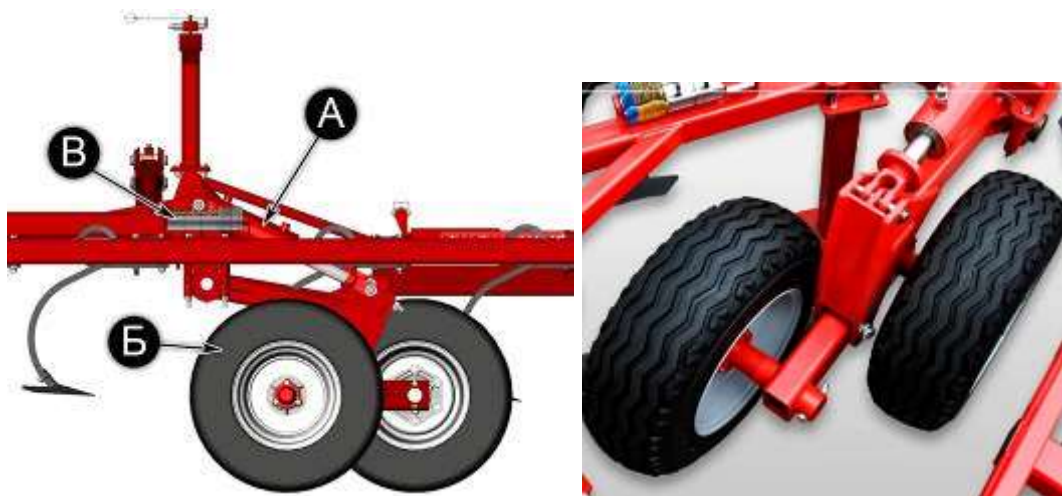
Схема для налаштування культиватора в робоче положення [5]
